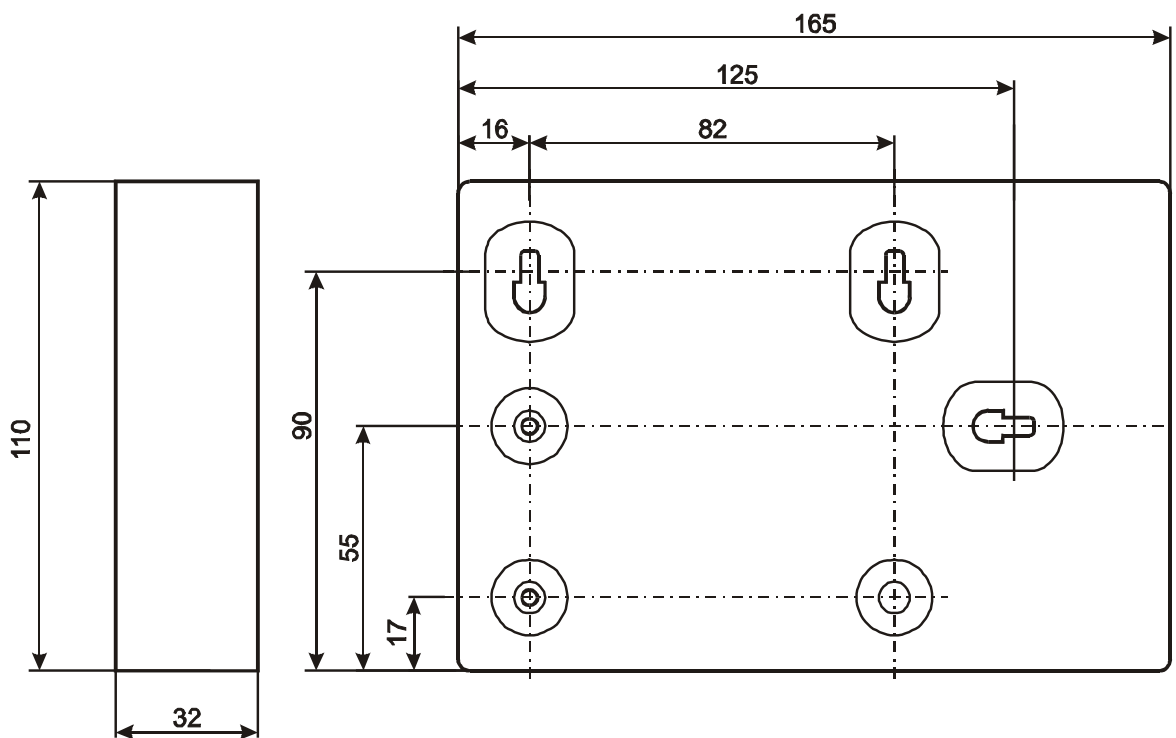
Габаритные и присоединительные размеры СК-01 исп.3 (корпус IP20)
